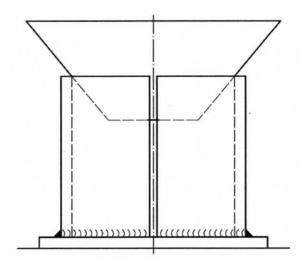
Подготовка и испытание на излом образцов угловых швов труб
